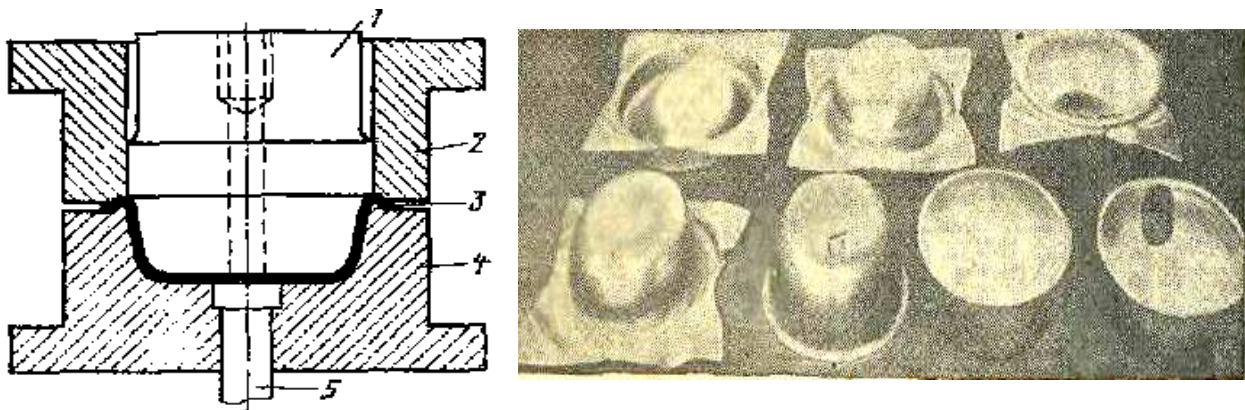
Схема витяжки і деталі, отримані витяжкою
